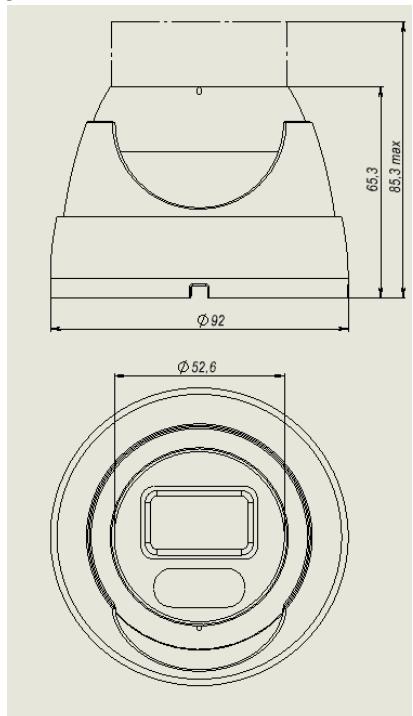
Внешний вид видеокамеры EVM2-IPx корпус KP23
